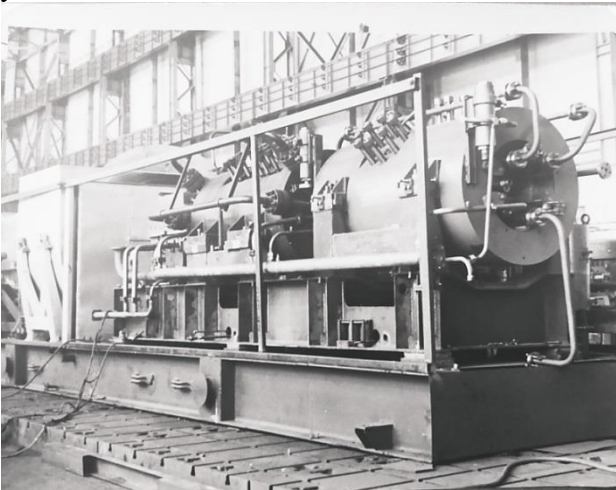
Двокорпусний компресорний агрегат установлення сайклінг процесу перед відвантаженням
